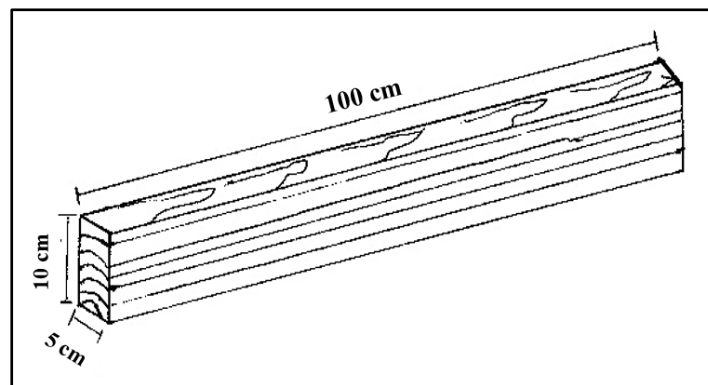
Dimensión de Probeta Destinada a Ensayos de Moldurado.
